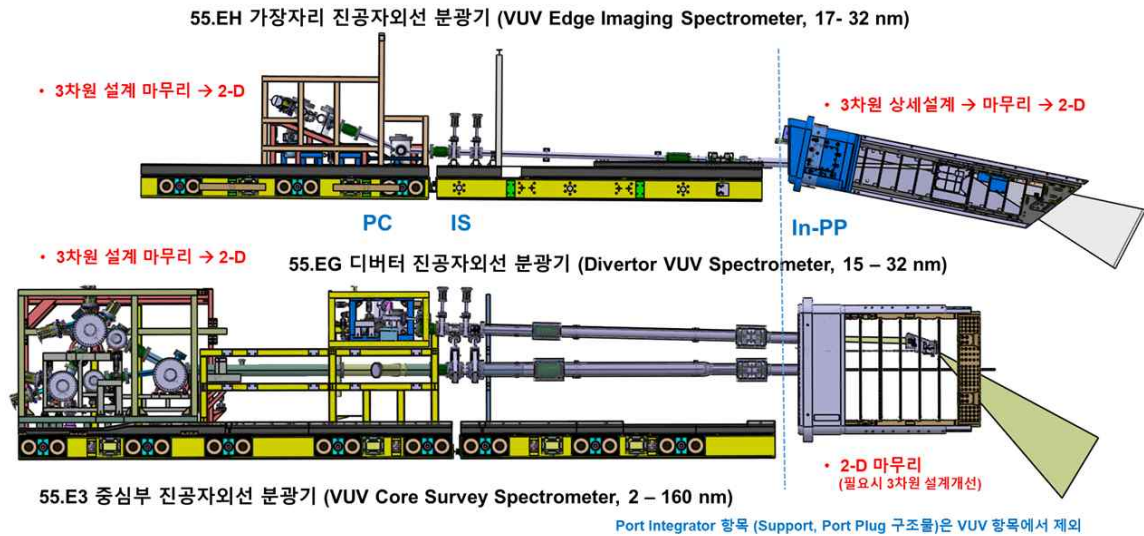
진공자외선 (VUV) 분광기 3종. 2-D 는 General Assembly Drawing 및 Installation Drawing을 의미.
